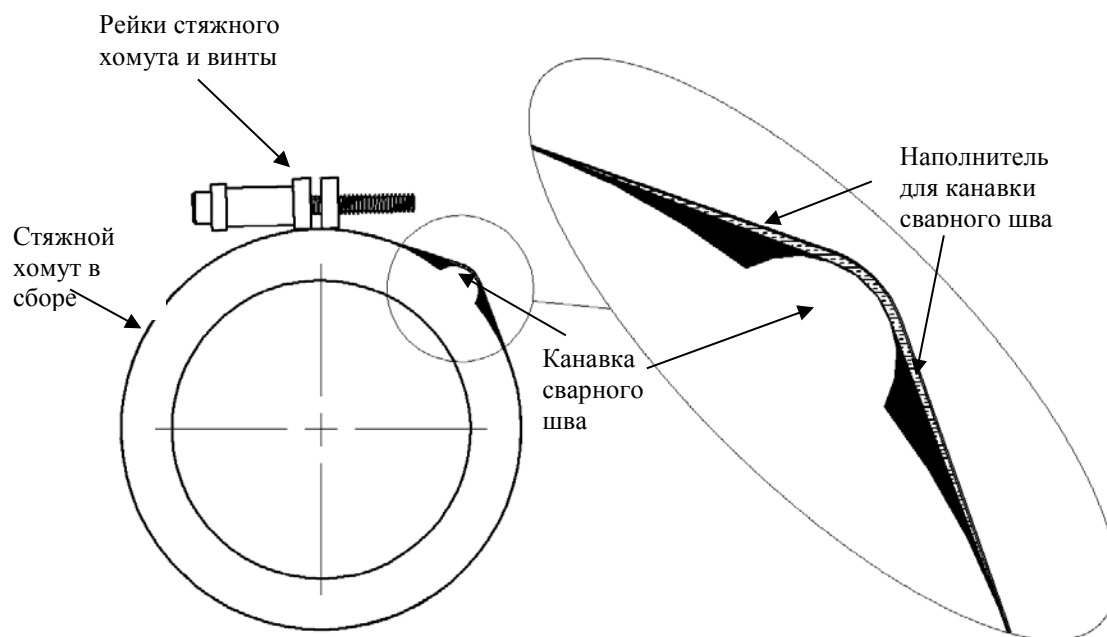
Наполнитель для канавки сварного шва
